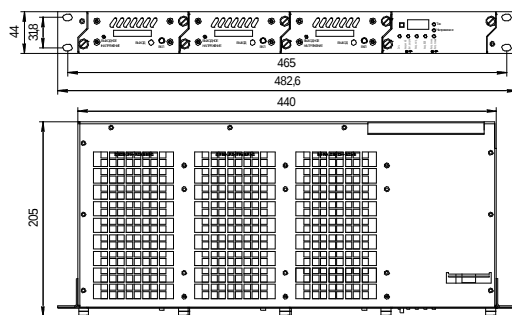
Габаритный чертеж УЭП-2К
